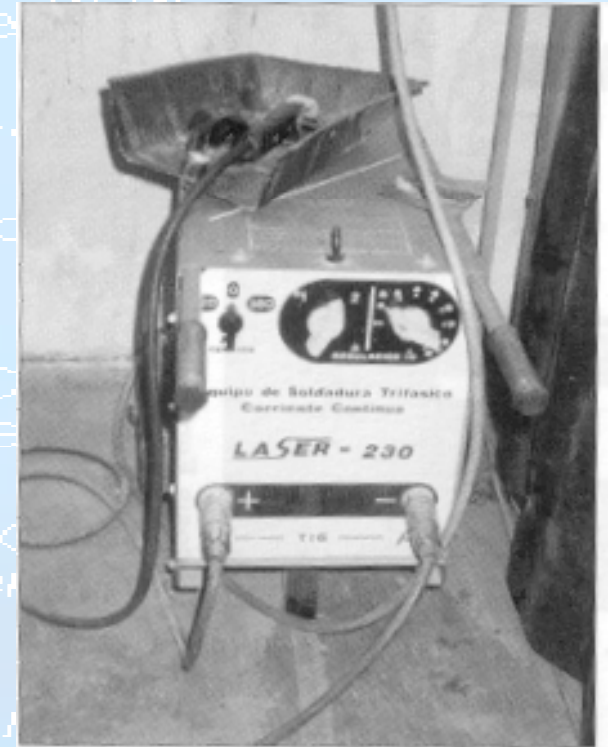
Soldadura por arco de electrodo revestido.
